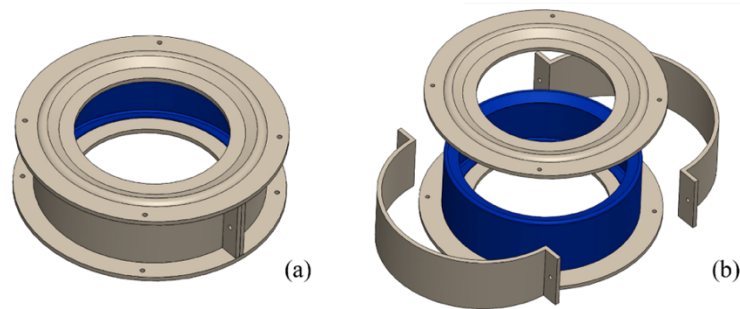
Esquema de montaje y particiones del molde desarrollado para la fabricación del casco de composite CFRE. (a) Molde ensamblado. (b) Desmoldeo del laminado curada.
